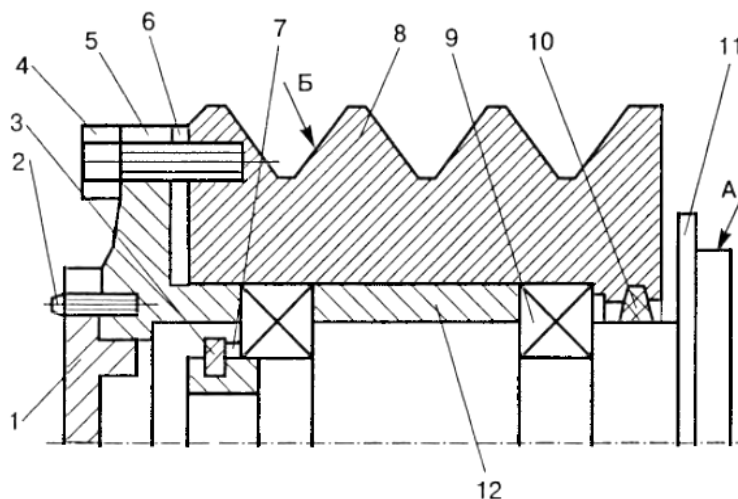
Эскиз ступицы: 1 - крышка; 2 - винт (4 шт.); 3 - шайба; 4 - винт; 5 - фланец; 6 - прокладка; 7 - кольцо компенсационное; 8 - шкив; 9 - подшипник (2 шт.); 10 - кольцо уплотнительное; 11 ступица; 12 – втулка
